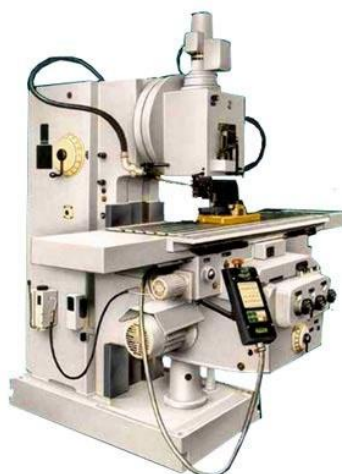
Вертикальный консольно-фрезерный станок с крестовым столом 6Т12.
